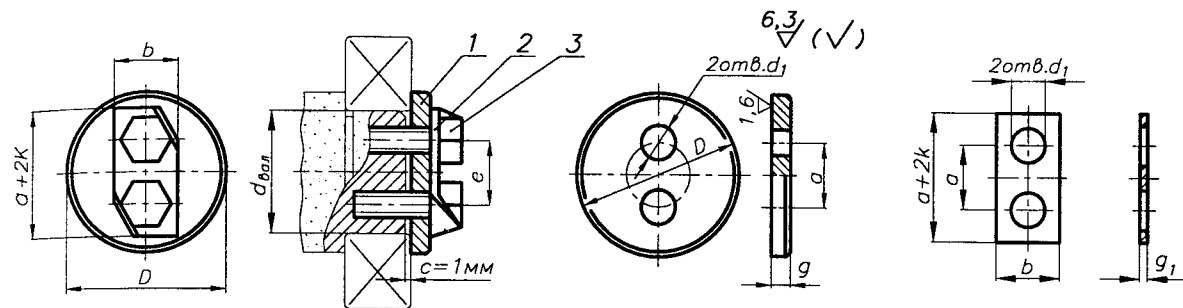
Закрепление подшипника на валу с использованием концевой шайбы:
